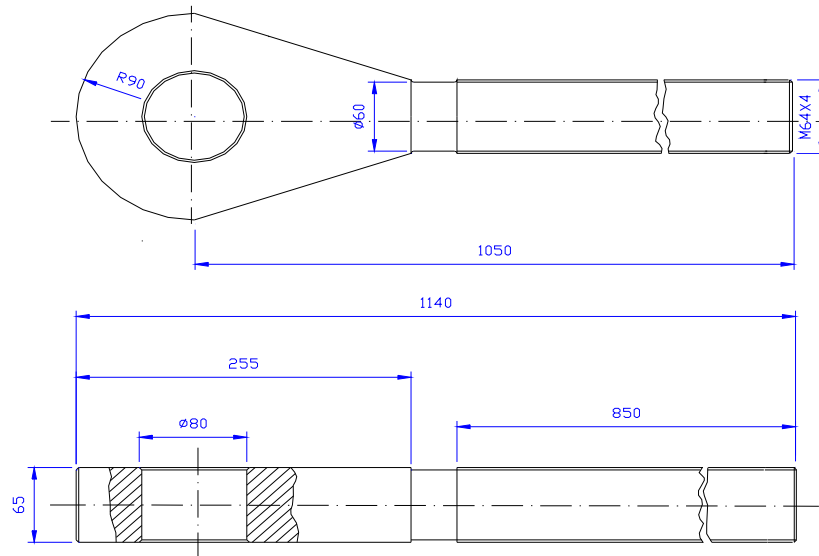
Чертёж регулировочного болта из стали 30ХМ, массой 36 кг
